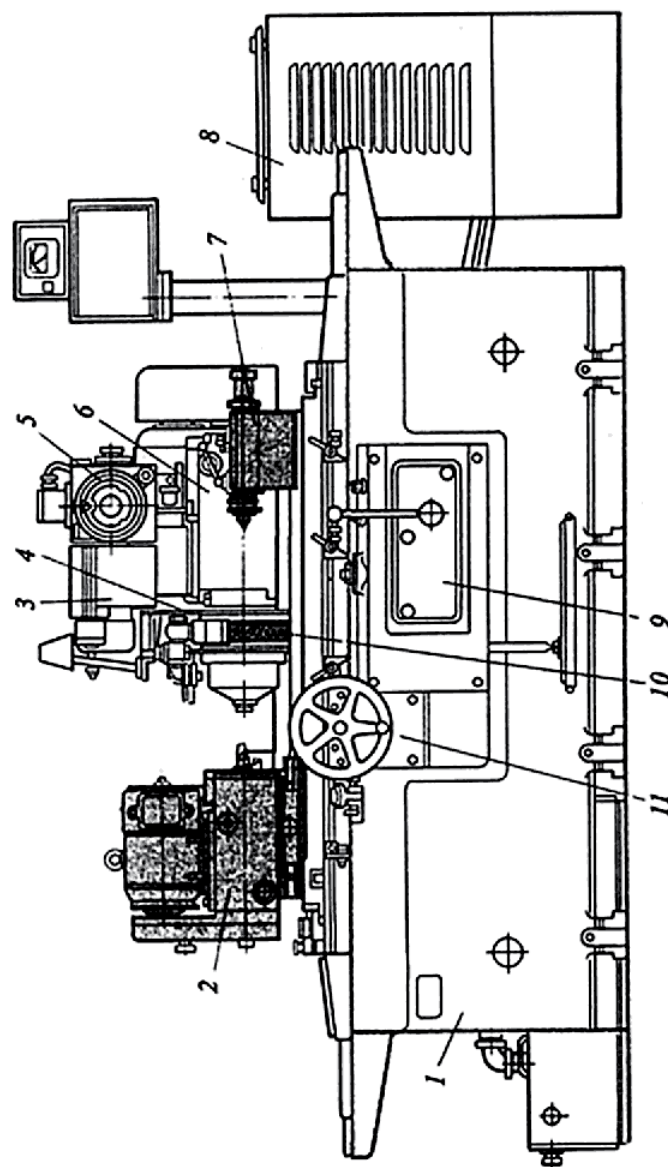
Круглошлифовальный станок мод. 3У131:
